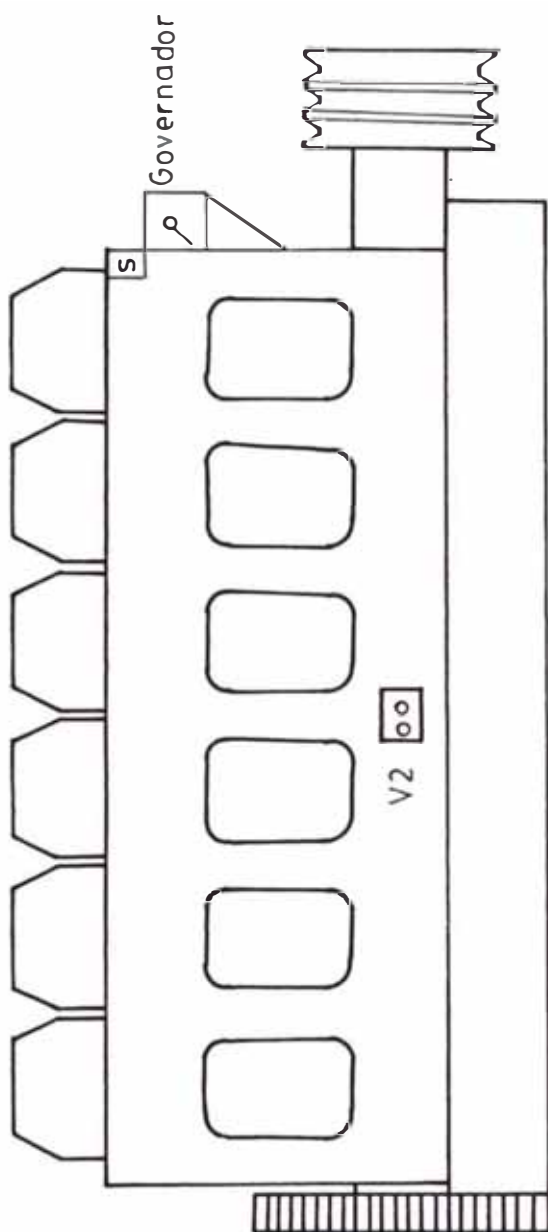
CONJUNTO DEL MONOBLOCK DEL MOTOR
